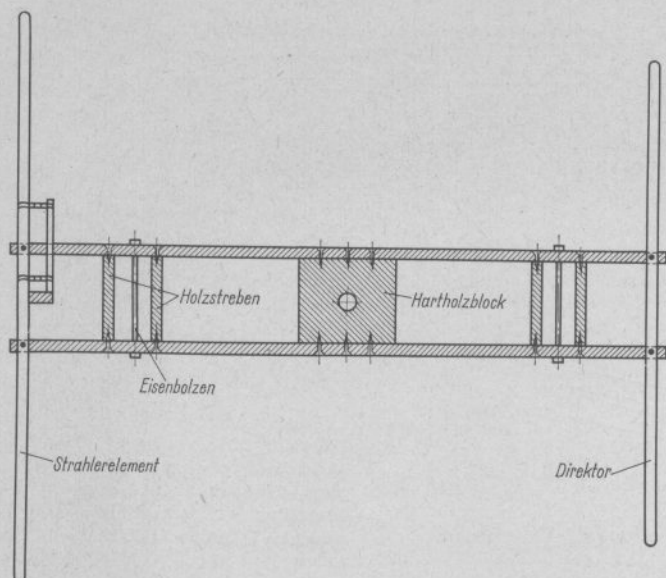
Holzkonstruktion als Tragegerüst für einen 2-Element-Richtstrahler
